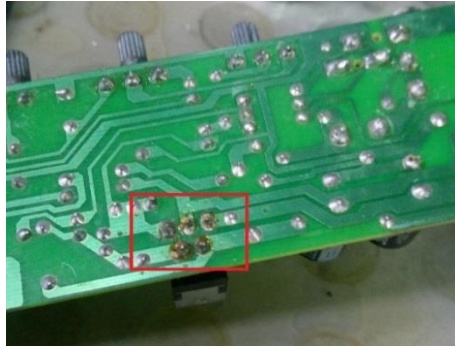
Soldadura del TDA2050 llena de líquido – Autoría propia
